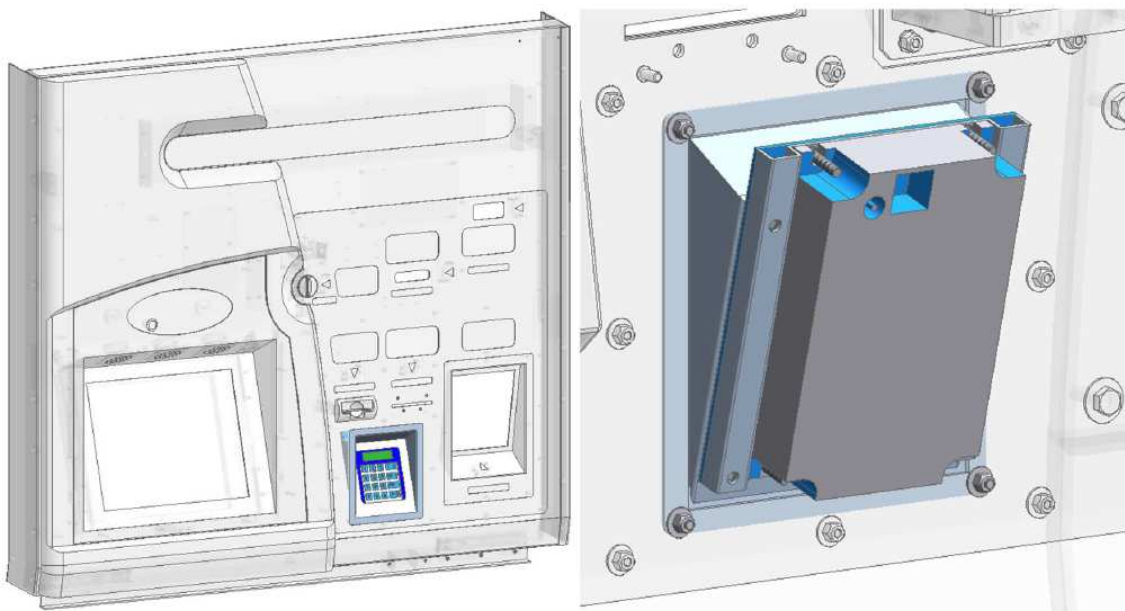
Elementos del conjunto PIN-PAD a retirar (METTA).
